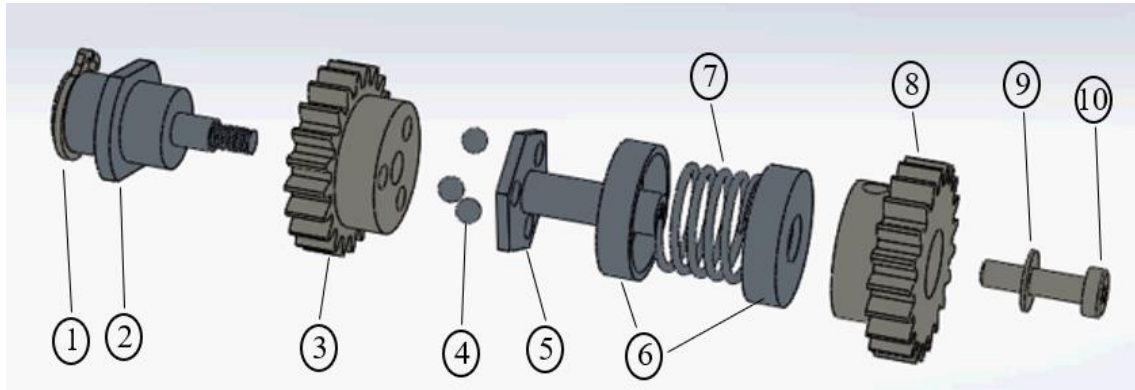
Embraiagem simples visão explodida: 1- Freio; 2-moente; 3-roda dentada do atuador; 4-esferas; 5-gaiola de esferas; 6-suporte da mola;7-mola; 8-roda dentada do motor; 9-anilha; 10-parafuso
